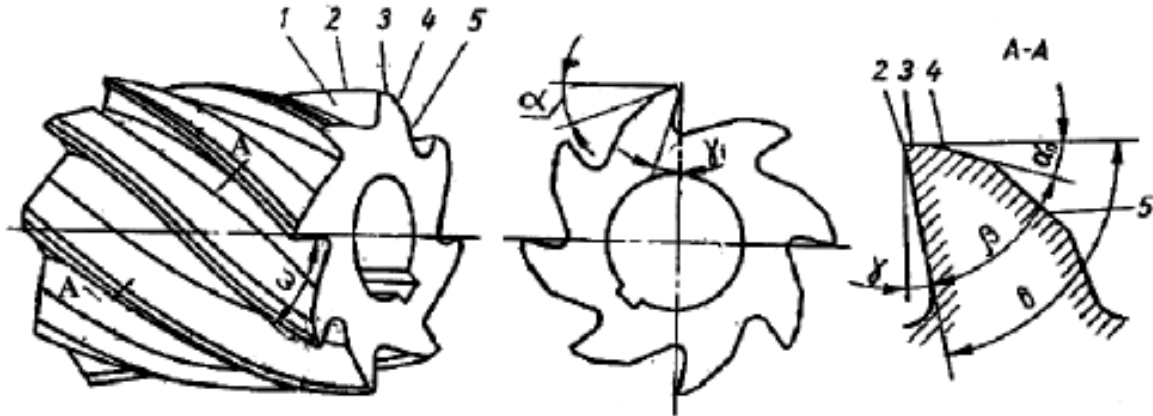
Циліндрична фреза: 1 - передня поверхня зуба; 2 - різальна кромка; 3 - фаска; 4 – задня поверхня зуба; 5 - затилкова поверхня; а - задній кут;  $\alpha_n$  – нормальний задній кут;  $\beta$  - кут загострення;  $\omega$  - кут нахилу гвинтової канавки;  $\gamma$  - передній кут;  $\gamma_1$  - поперечний передній кут
